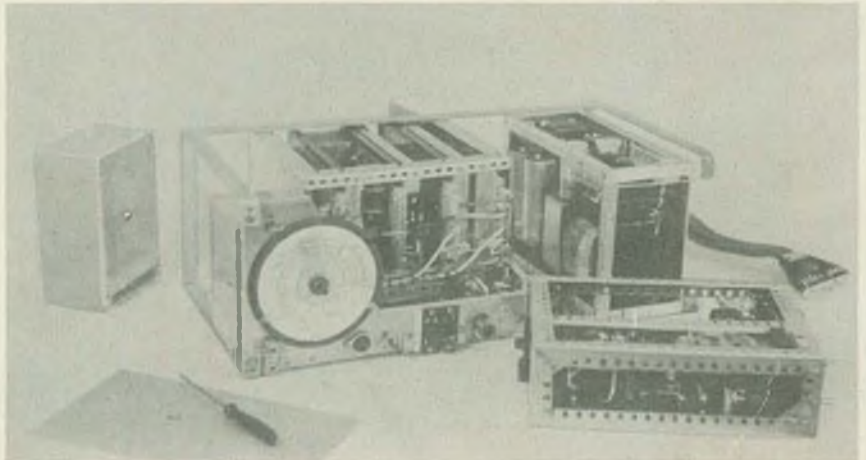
Der Einschubrahmen wurde aus Flacheisen geschweißt, alle Baustufen sind bequem zugänglich. Mit Adapter-schnüren können die Baugruppen auch außerhalb der Aufnahmevorrichtung überprüft werden
